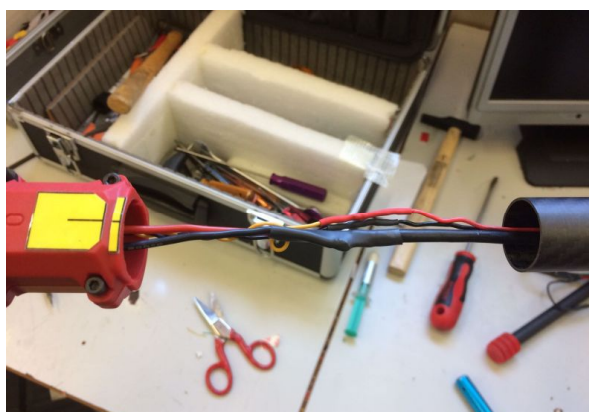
Soldadura de los cables del variador y los del frame.
